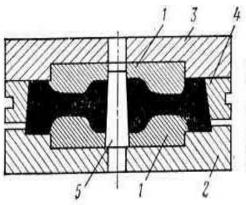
Схема закрытого штампа гидравлического пресса для изготовления поковок вагонных колес: 1 — рабочие вставки для ступицы; 2 — нижний штамп; 3 — верхний штамп; 4 —вставка для обода; 5 — прошивень
